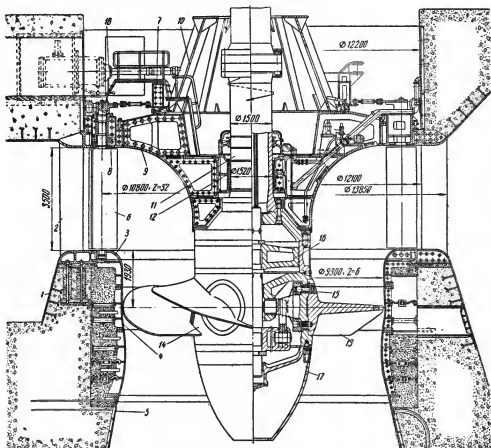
Разрез поворотнлопастной турбины мощностью 115 тыс. кВт и $D_1=9,3$ м. 1 — облицовка спирали; 2 — статор; 3 — нижнее кольцо направляющего аппарата; 4 — камера рабочего колеса; 5 — облицовка отсасывающей трубы; 6 — лопатка направляющего аппарата; 7 — регулирующее кольцо; 8 — верхнее кольцо направляющего аппарата; 9 — крышка турбины; 10 — опора подпятника; 11 — вал; 12 — подшипник; 13 — рабочая лопасть; 14 — ступка колеса; 15 — уплотнение лопасти; 16 — сервомотор рабочего колеса; 17 — обтекатель; 18 — сервомотор направляющего аппарата.
